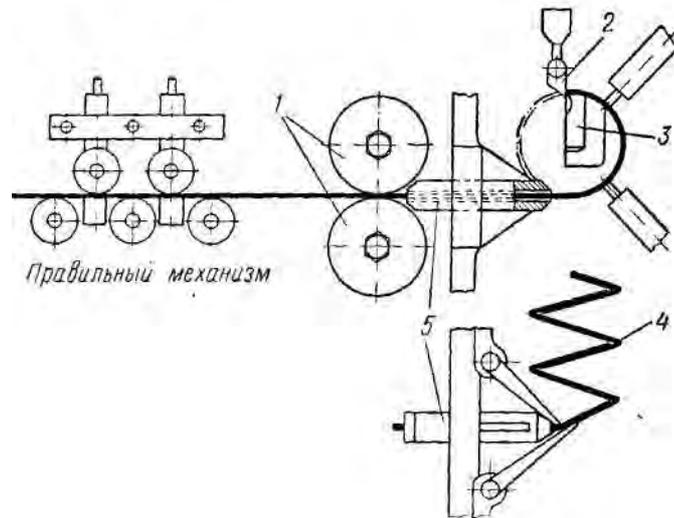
Схема безоправочной навивки пружин на станке-автомате:
